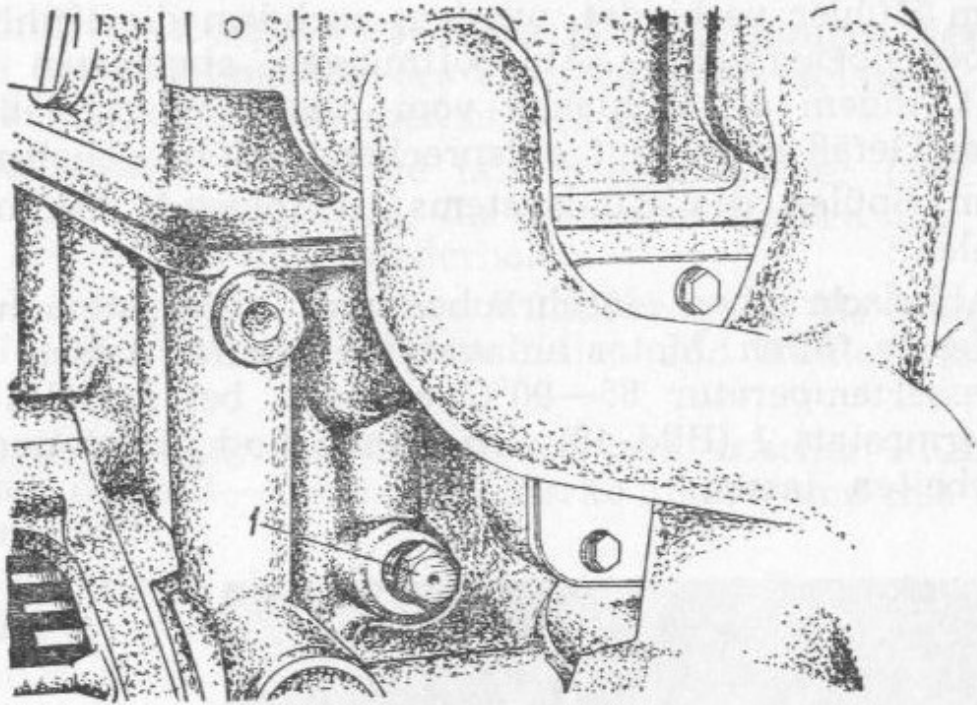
Anordnung der Ablasschraube am Kühlmantel des Zylinderblocks :
